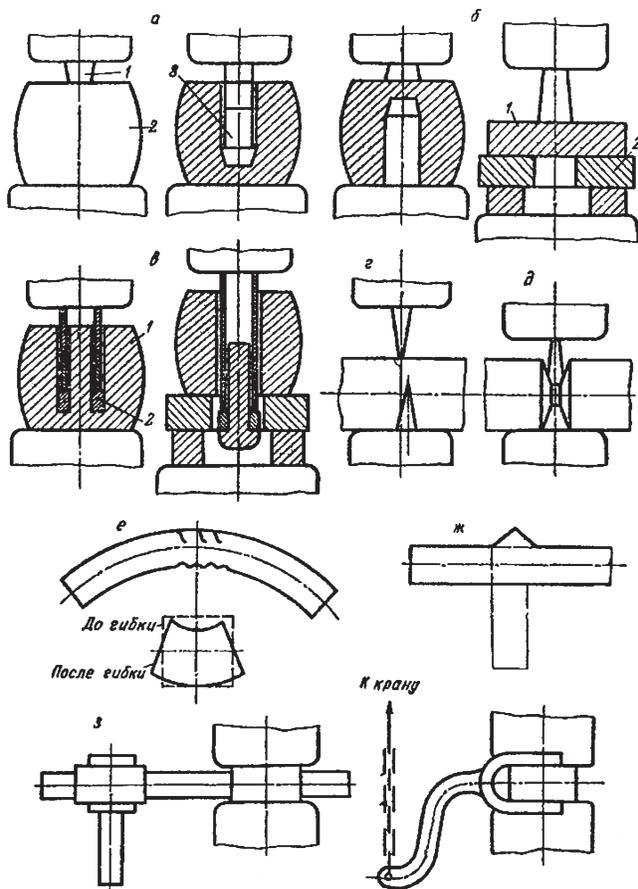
Прошивка, рубка, гибка и закручивание: а – прошивка без подкладного кольца; б – прошивка с подкладным кольцом; в – прошивка пустотелым прошивнем; г – рубка с двух сторон; д – рубка с четырех сторон; е – гибка; ж – увеличение поперечных размеров при гибке; з – закручивание вокруг общей оси
